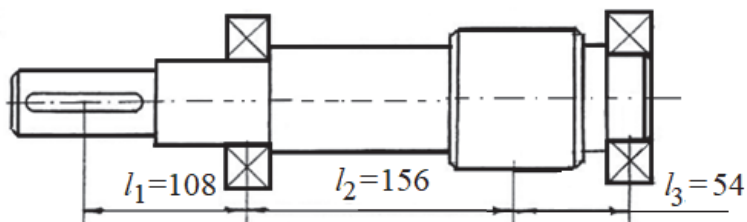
Графический чертёж детали – быстроходного вала (размеры приводятся в мм)
